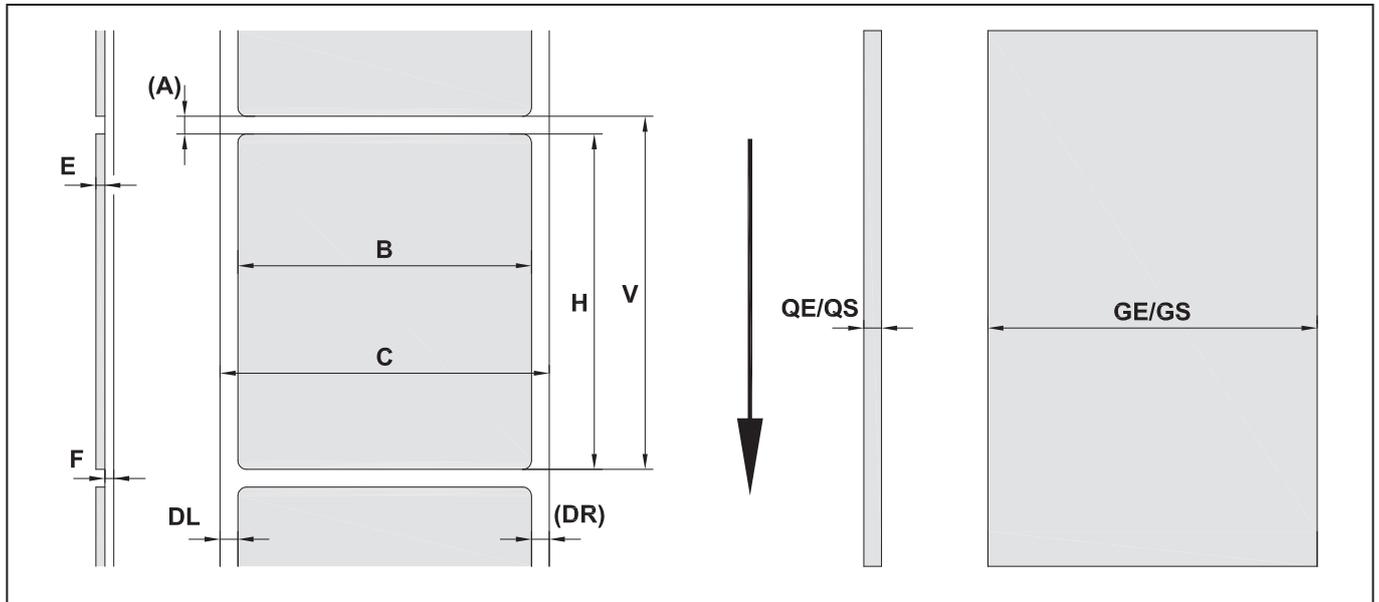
Dimensiones del material, \* = sentido de marcha
